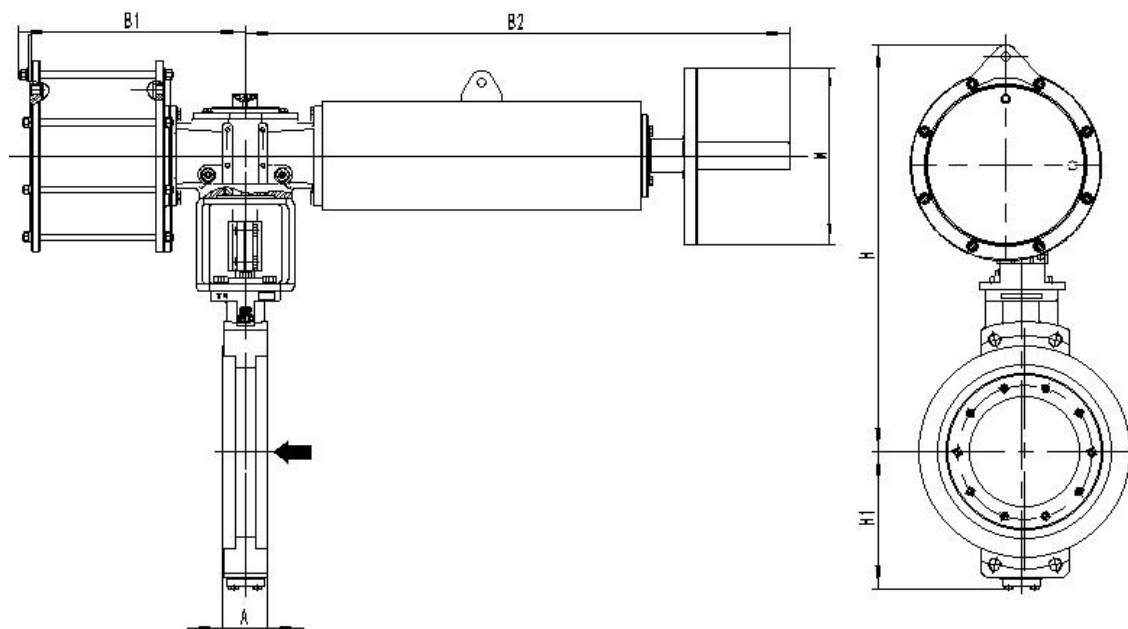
配 AW18SR41~AW27SR52 带丝杆手轮外形尺寸图 (FC)
